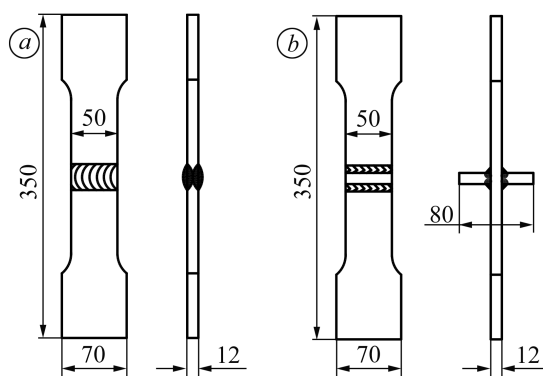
Форма и геометрические размеры стыкового (*a*) и таврового (*b*) образцов сварных соединений.
